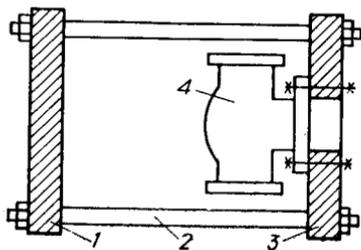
Приспособление для проточки седла клапана вентиля:
